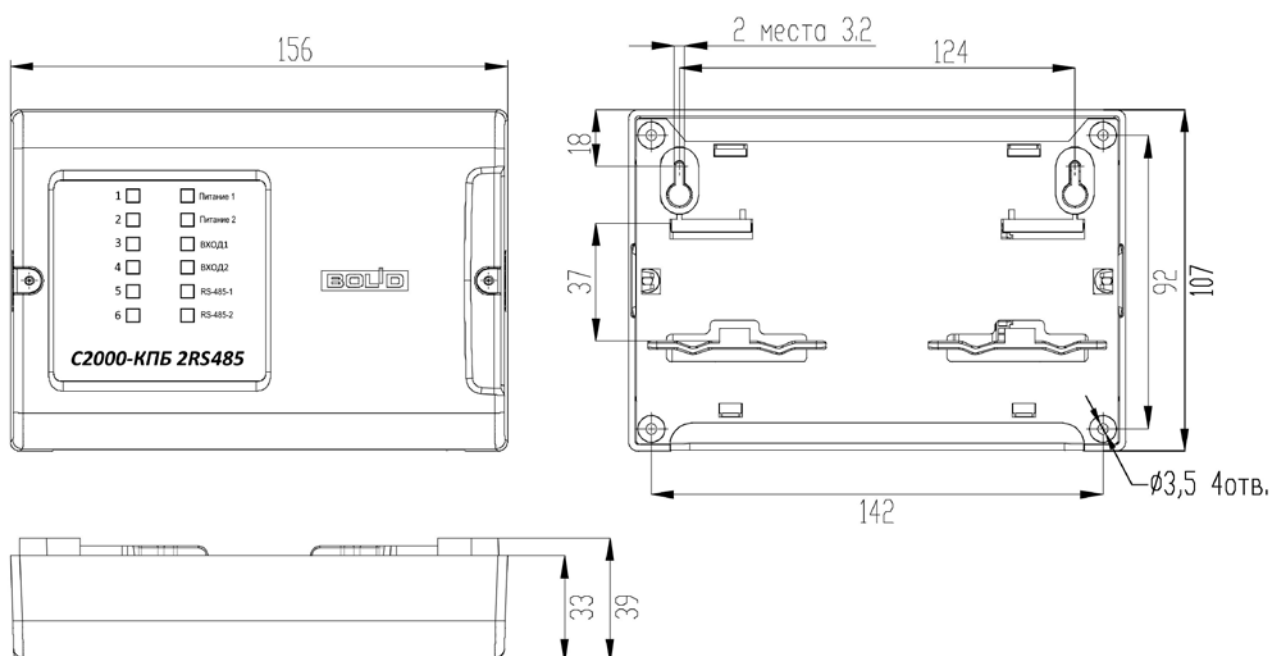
Внешний вид и габаритно-установочные размеры блока.
